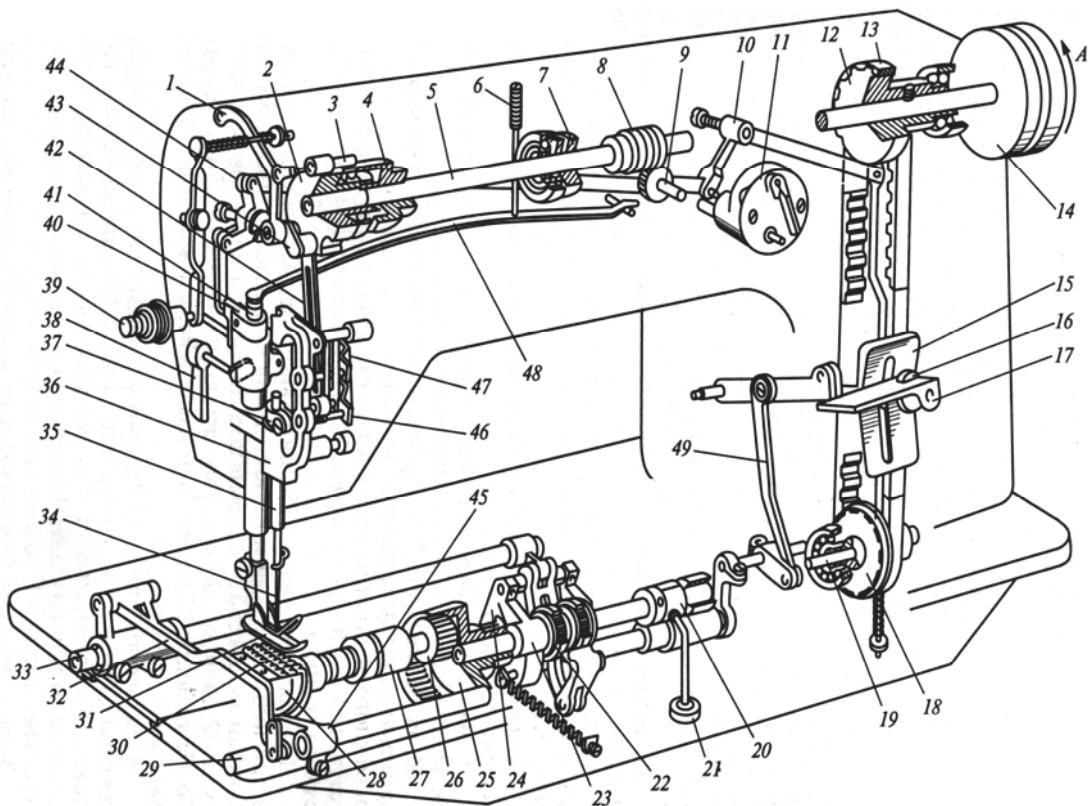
Конструктивно-кінематична схема механізмів швейної машини КУР-31-12+3:
